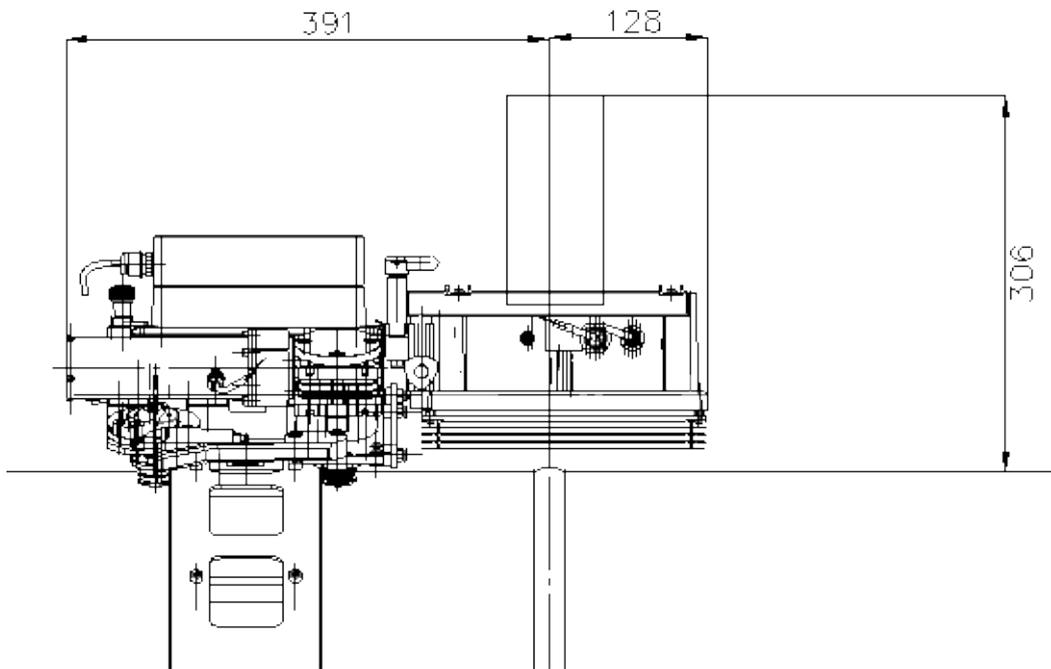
Габаритные размеры блока детектора комплекса Транскан с установленным модулем ВИЗИО МТ. Минимальный зазор от габаритов Комплекса до земли или элементов трубопровода – 50 мм.
